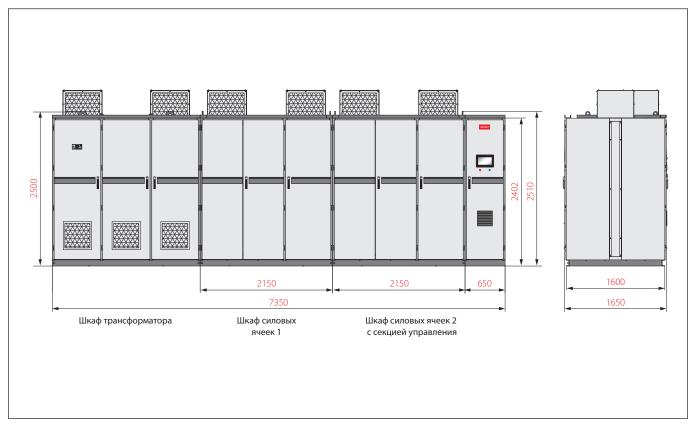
Корпуса DA05 и DB05 на напряжение 6 и 6,6 кВ
